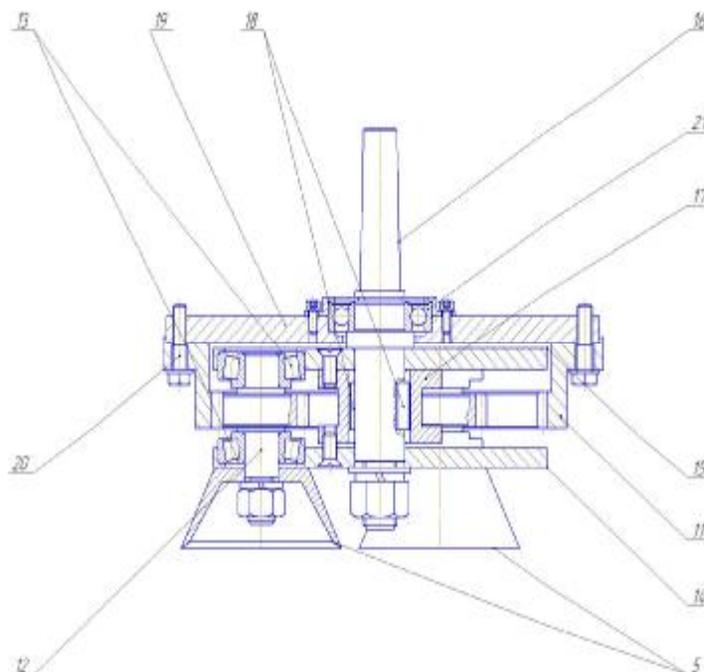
Устройство планетарной головки для точения наружной цилиндрической поверхности вала.
